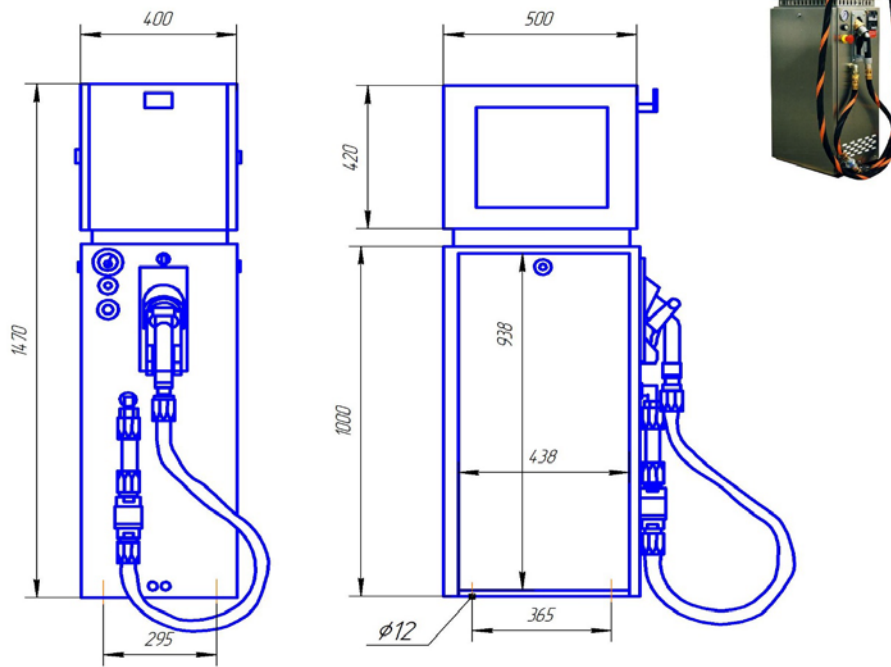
Установка газораздаточной колонки УЗСГ-01. Общий вид
